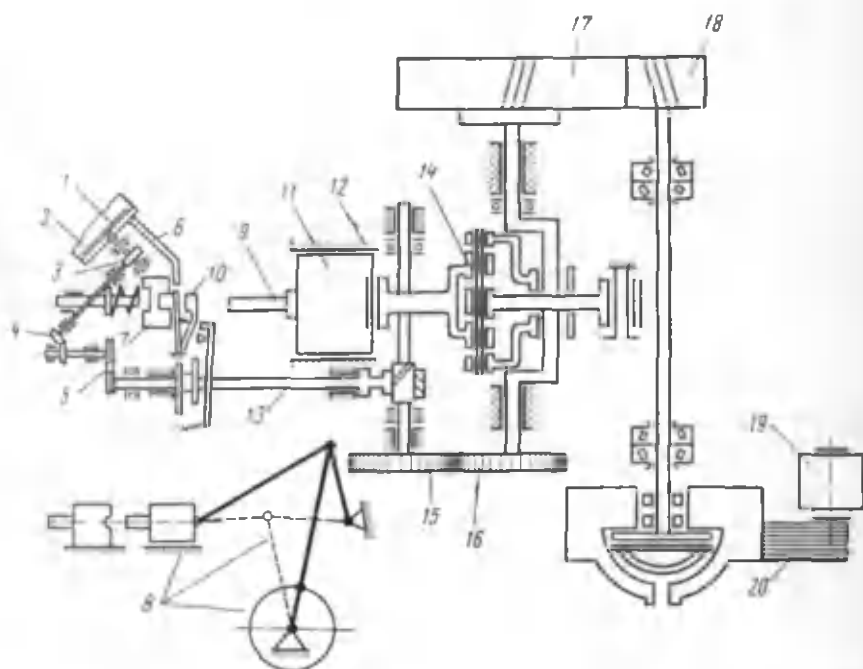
Кинематическая схема колено-рычажного пресса для вытяжки цилиндрических цинковых стаканов:
